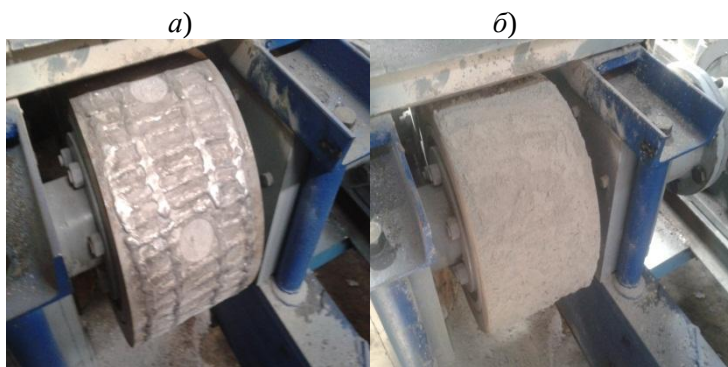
Валки ПВИ с наплавленной футерующей сеткой на их рабочей поверхности:
